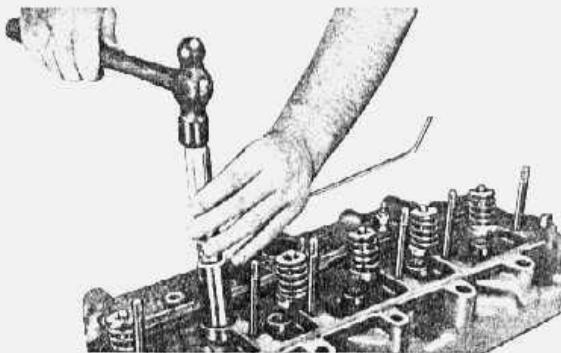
instalação das guias das válvulas de admissão (motor de 6 cilindros)
